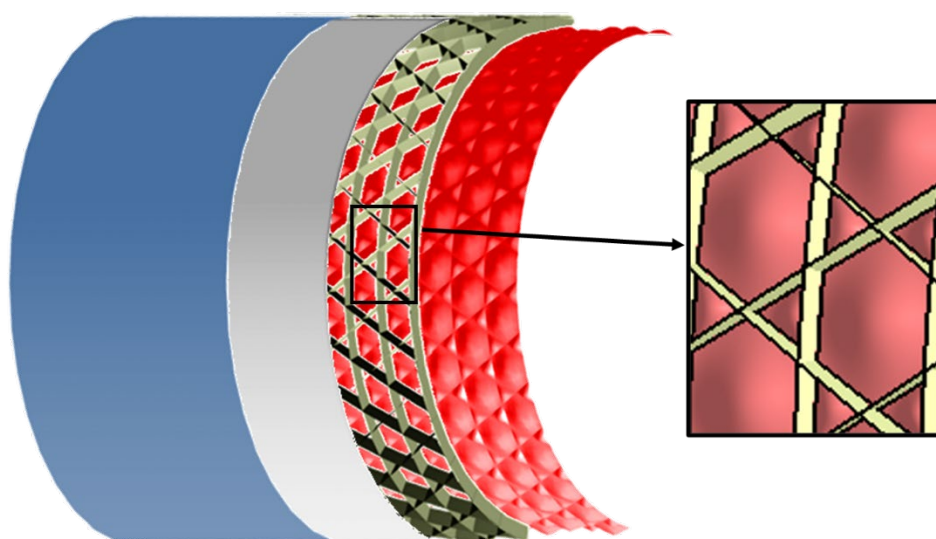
Сетчатый композитный отсек с защитой и полужесткой обшивкой для передачи наддува
